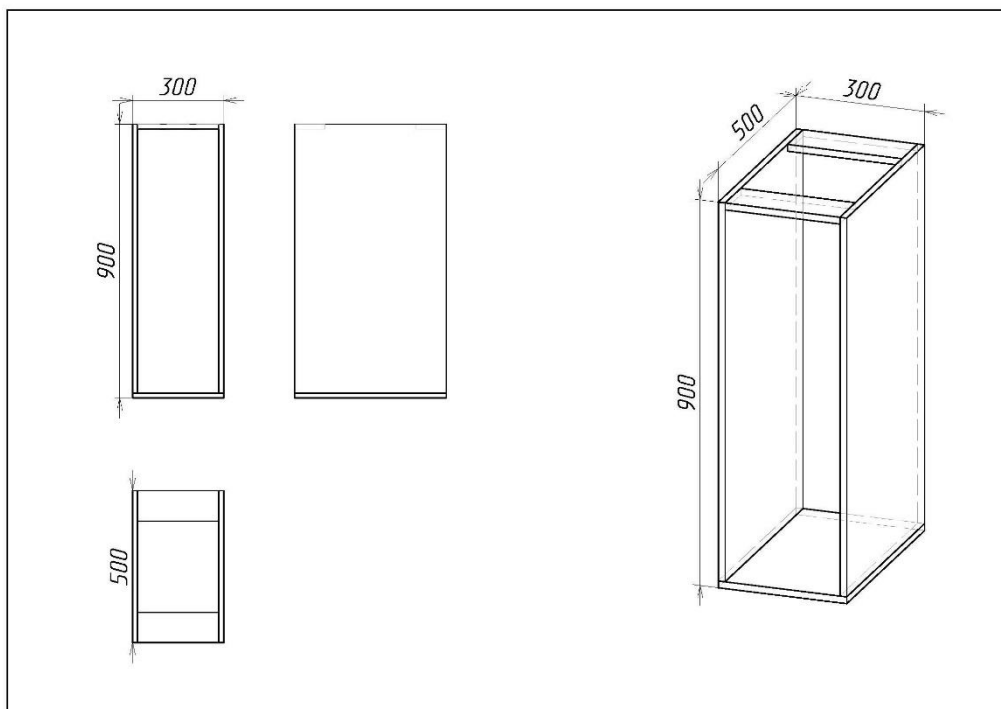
Корпус - Крышка или царги вкладные, дно накладное относительно боков (БМ)
